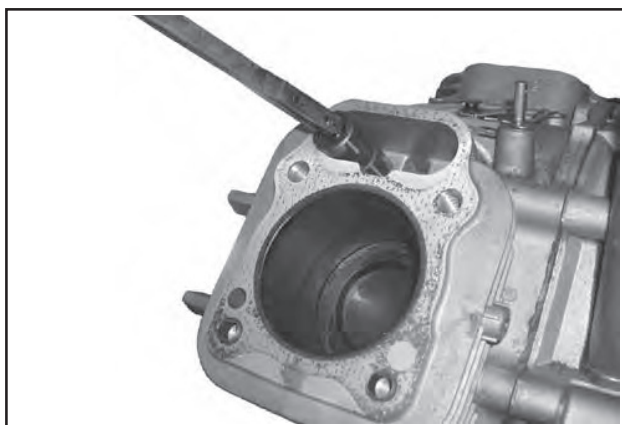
Ausbau der hydraulischen Stößel.
